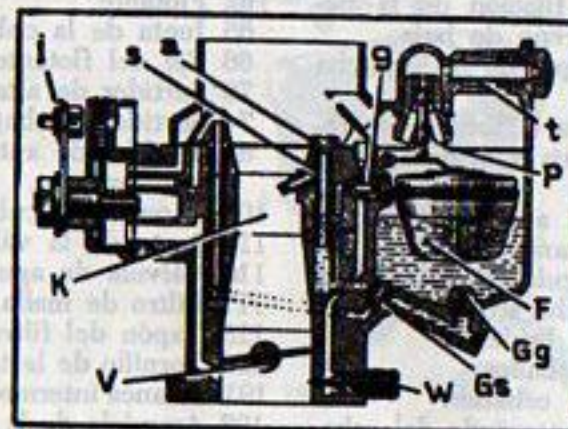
Disposición de los elementos de los carburadores Solex 28 CBI y 28 IBC.
